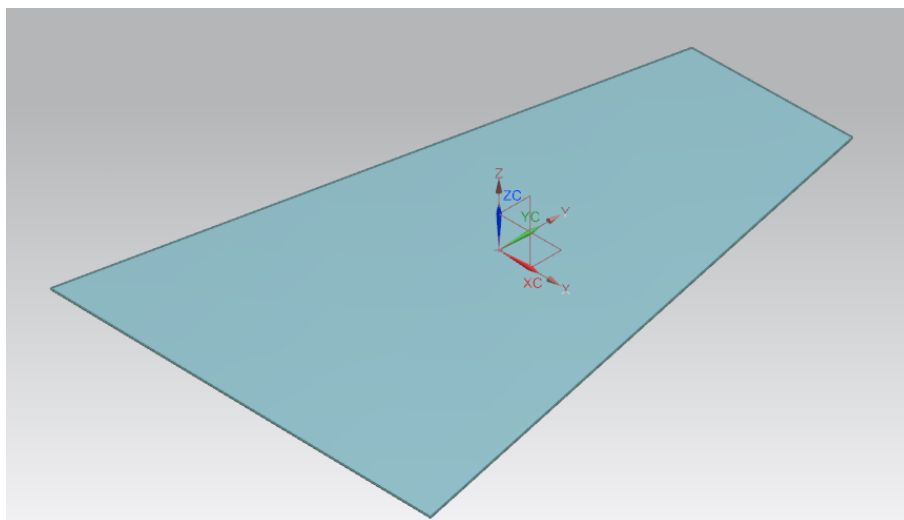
Полуфабрикат (исходная заготовка) для изготовления деталей
